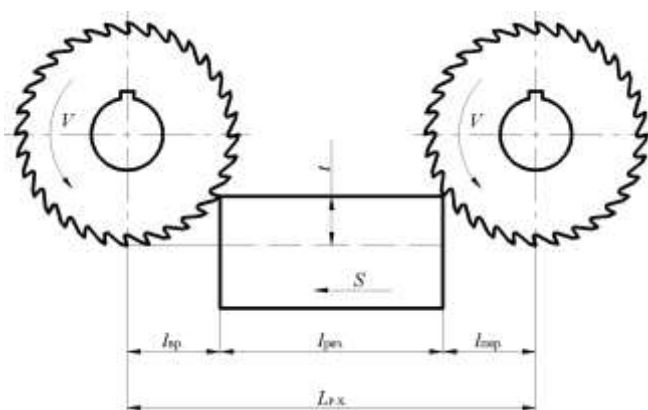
Длина рабочего хода инструмента при фрезеровании
